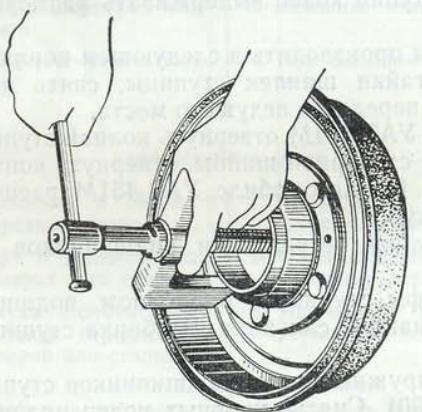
Выпрессовка наружных колец подшипников ступицы
